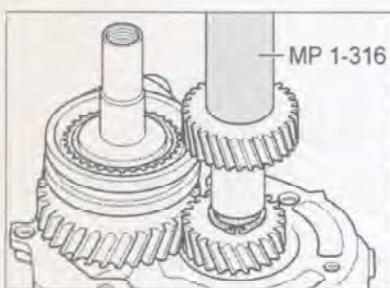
Нагрев шестерни 5-й передачи до 100°C, напрессуйте шестернию до упора на вал. Буртик шестерни должен быть направлен к корпусу подшипников.
